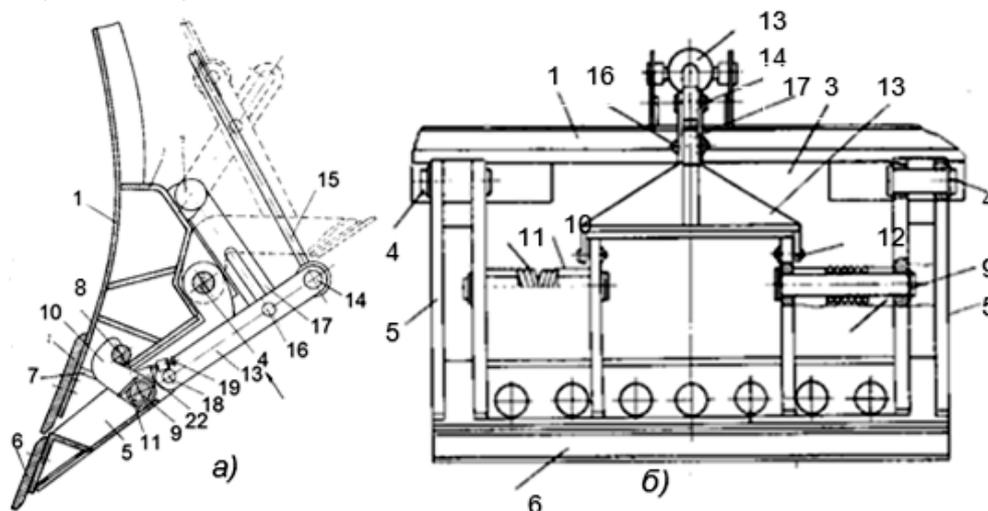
Бульдозерное оборудование в разрезе (а) и вид А (б): 1 - отвал; 2 - режущий элемент; 3 - коробка жесткости; 4 - пальцы; 5 - кронштейн; 6 - дополнительный режущий элемент; 7 - окна; 8 - цилиндрические опоры; 9 - пальцы; 10 - подпружиненные крюки; 11 - цилиндрические пружины кручения; 12 - пальцы; 13 - рычаги; 14 - палец; 15 - шток силового цилиндра; 16 - пальцы; 17 - продольное окно кулисы; 18 - проушина; 19 - регулируемые винтовые упоры; 20 - приливы
